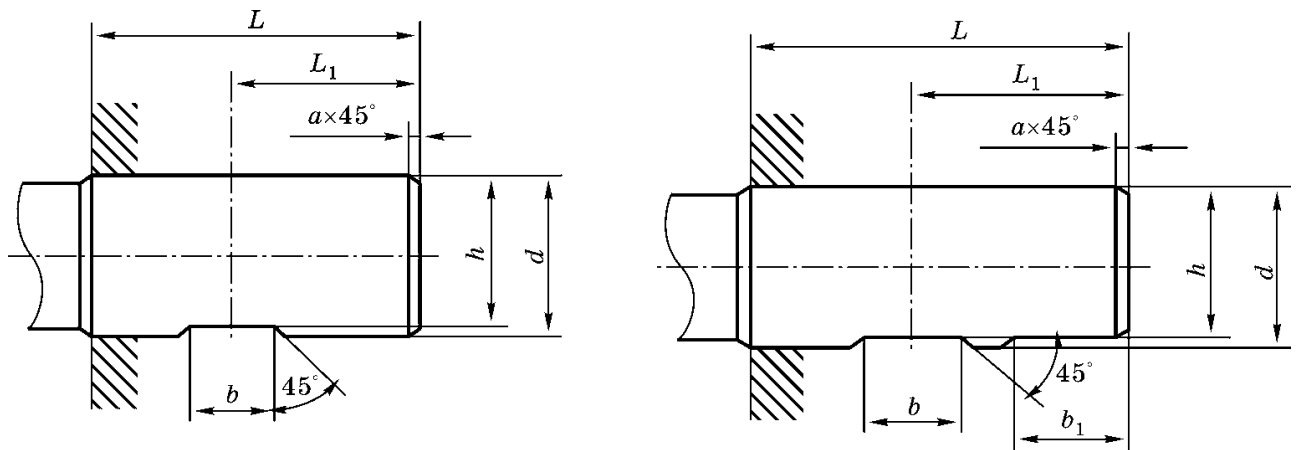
Циліндричний хвостовик типу WELDON [6]
